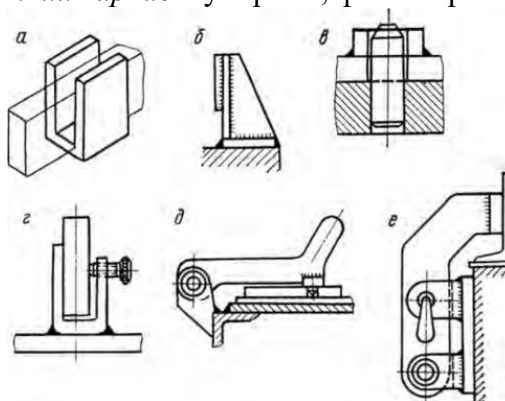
Элементы сборочных приспособлений: *a* — карман; *б* — упор; *в* — палец; *г* — зажим; *д* — палец откидной; *е* — упор откидной
